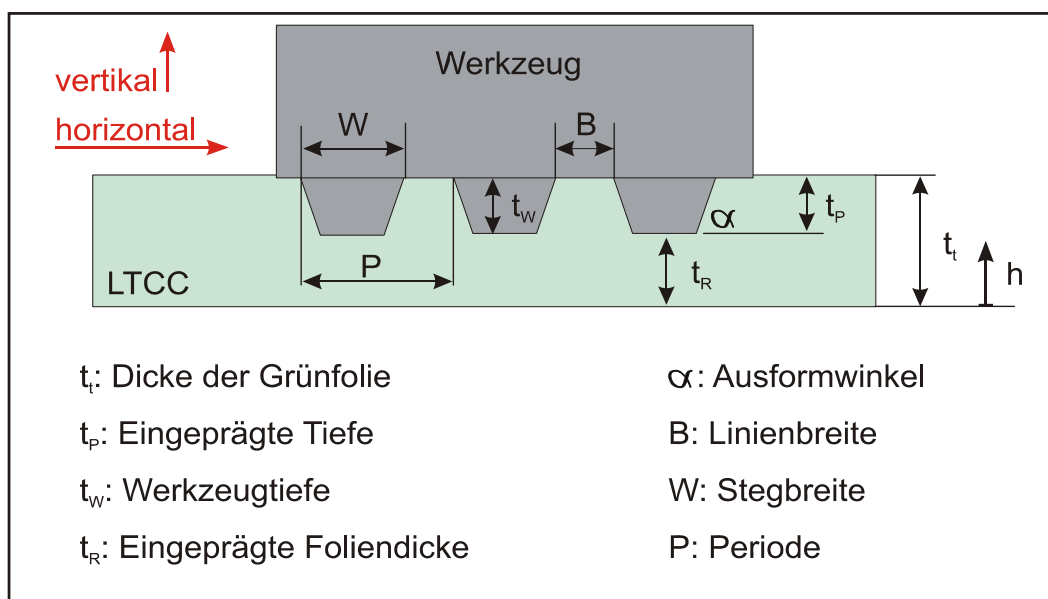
Profilquerschnitt durch das Prägewerkzeug.
